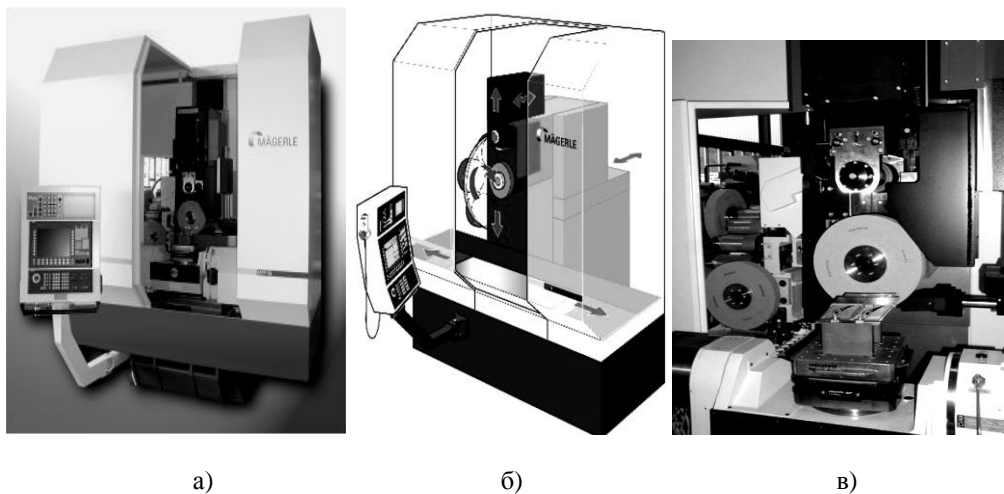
Общий вид профишлифовального станка *MFP-050.65.65* – а), схемы 5-ти осевой обработки и зоны шлифования, непрерывной правки алмазным роликом и автоматической смены шлифовальных кругов для профильного глубинного шлифования лопаток турбины
